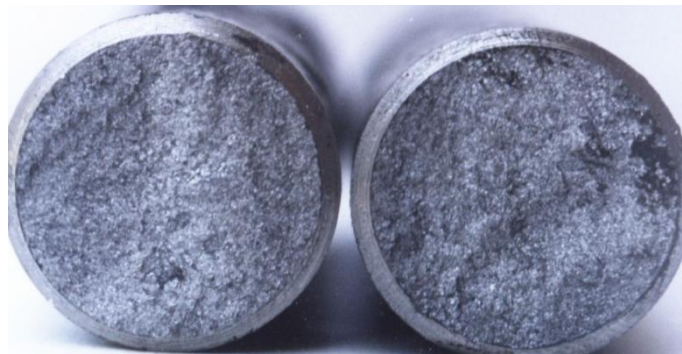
Заготовки из стали 30 при статико-динамическом нагружении
